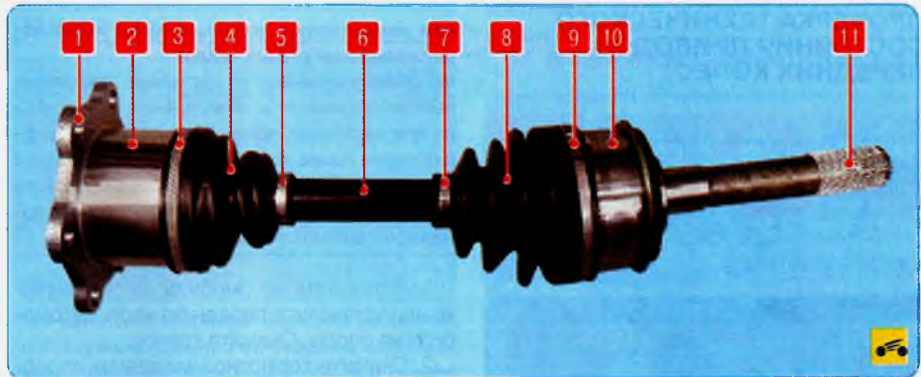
Привод переднего колеса: 1 – фланец крепления; 2 – внутренний шарнир; 3, 9 – большие хомуты крепления чехлов шарниров; 4 – чехол внутреннего шарнира; 5, 7 – малые хомуты крепления чехлов шарниров; 6 – вал привода; 8 – чехол наружного шарнира; 10 – наружный шарнир равных угловых скоростей; 11 – шлицевый наконечник корпуса наружного шарнира
